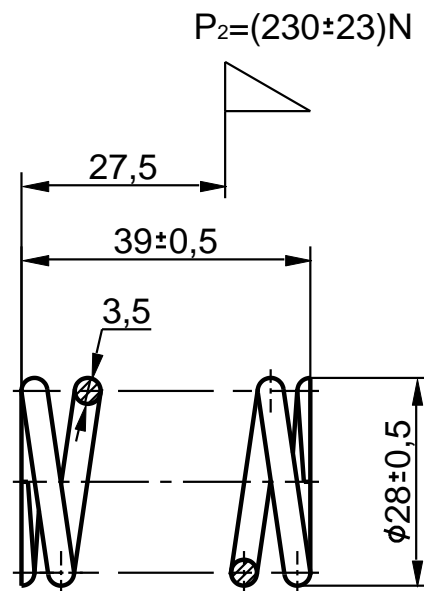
Пружина тормоза для механизма МЭО-1600
